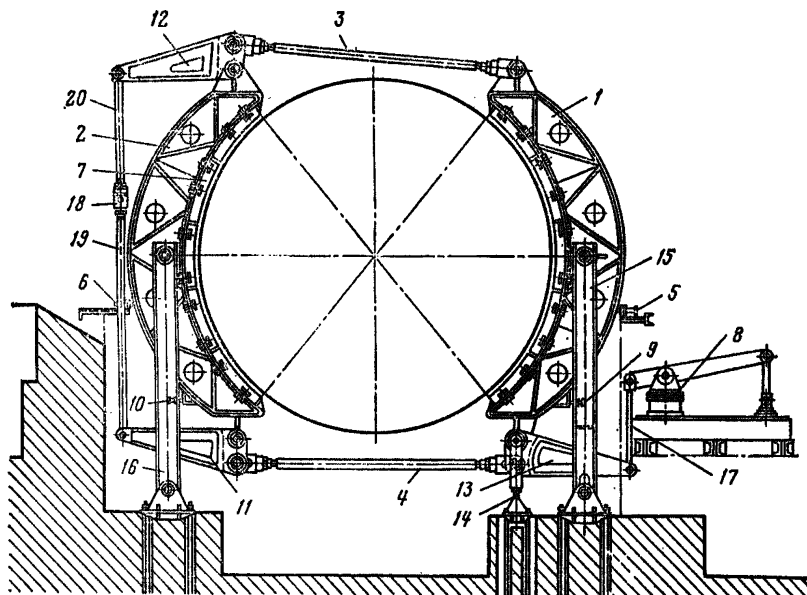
Схема исполнительного органа тормоза подъемных машин НКМЗ (III типа); 1, 2 — передняя и задняя тормозные балки; 3, 4 — верхняя и нижняя горизонтальные тяги; 5, 6 — верхние передний и задний упоры; 7 — колодки; 8 — цилиндр рабочего торможения; 9, 10 — нижние передний и задний упоры; 11, 12, 13 — рычаги; 14 — дополнительная стойка; 15, 16 — стойки; 17 — вертикальная тяга; 18 — га йка; 19, 20 — вертикальные тяги
